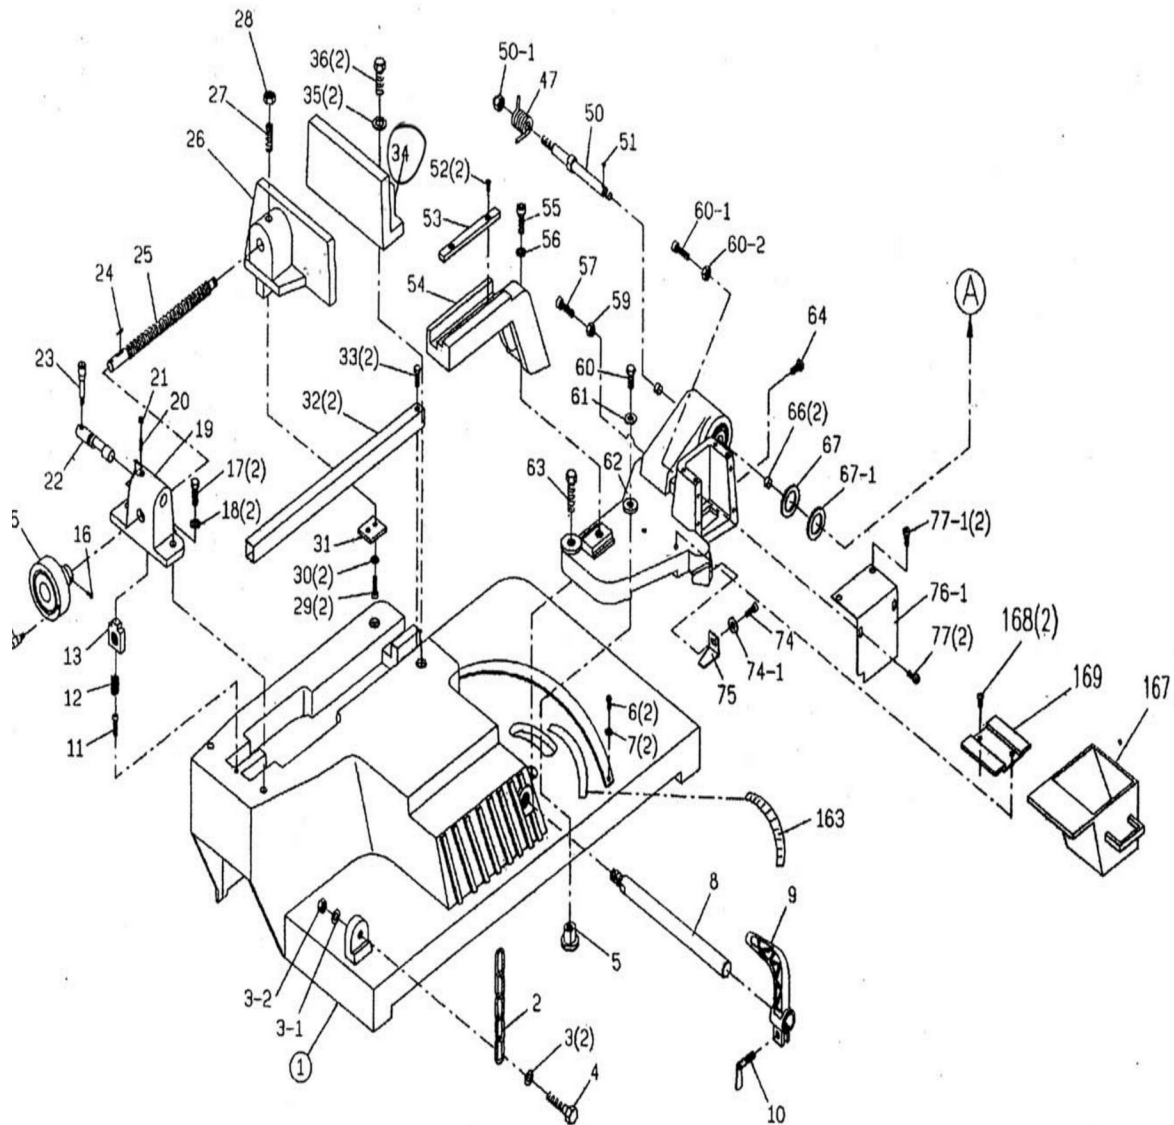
Vue éclatée — socle, étau et base pivotante
